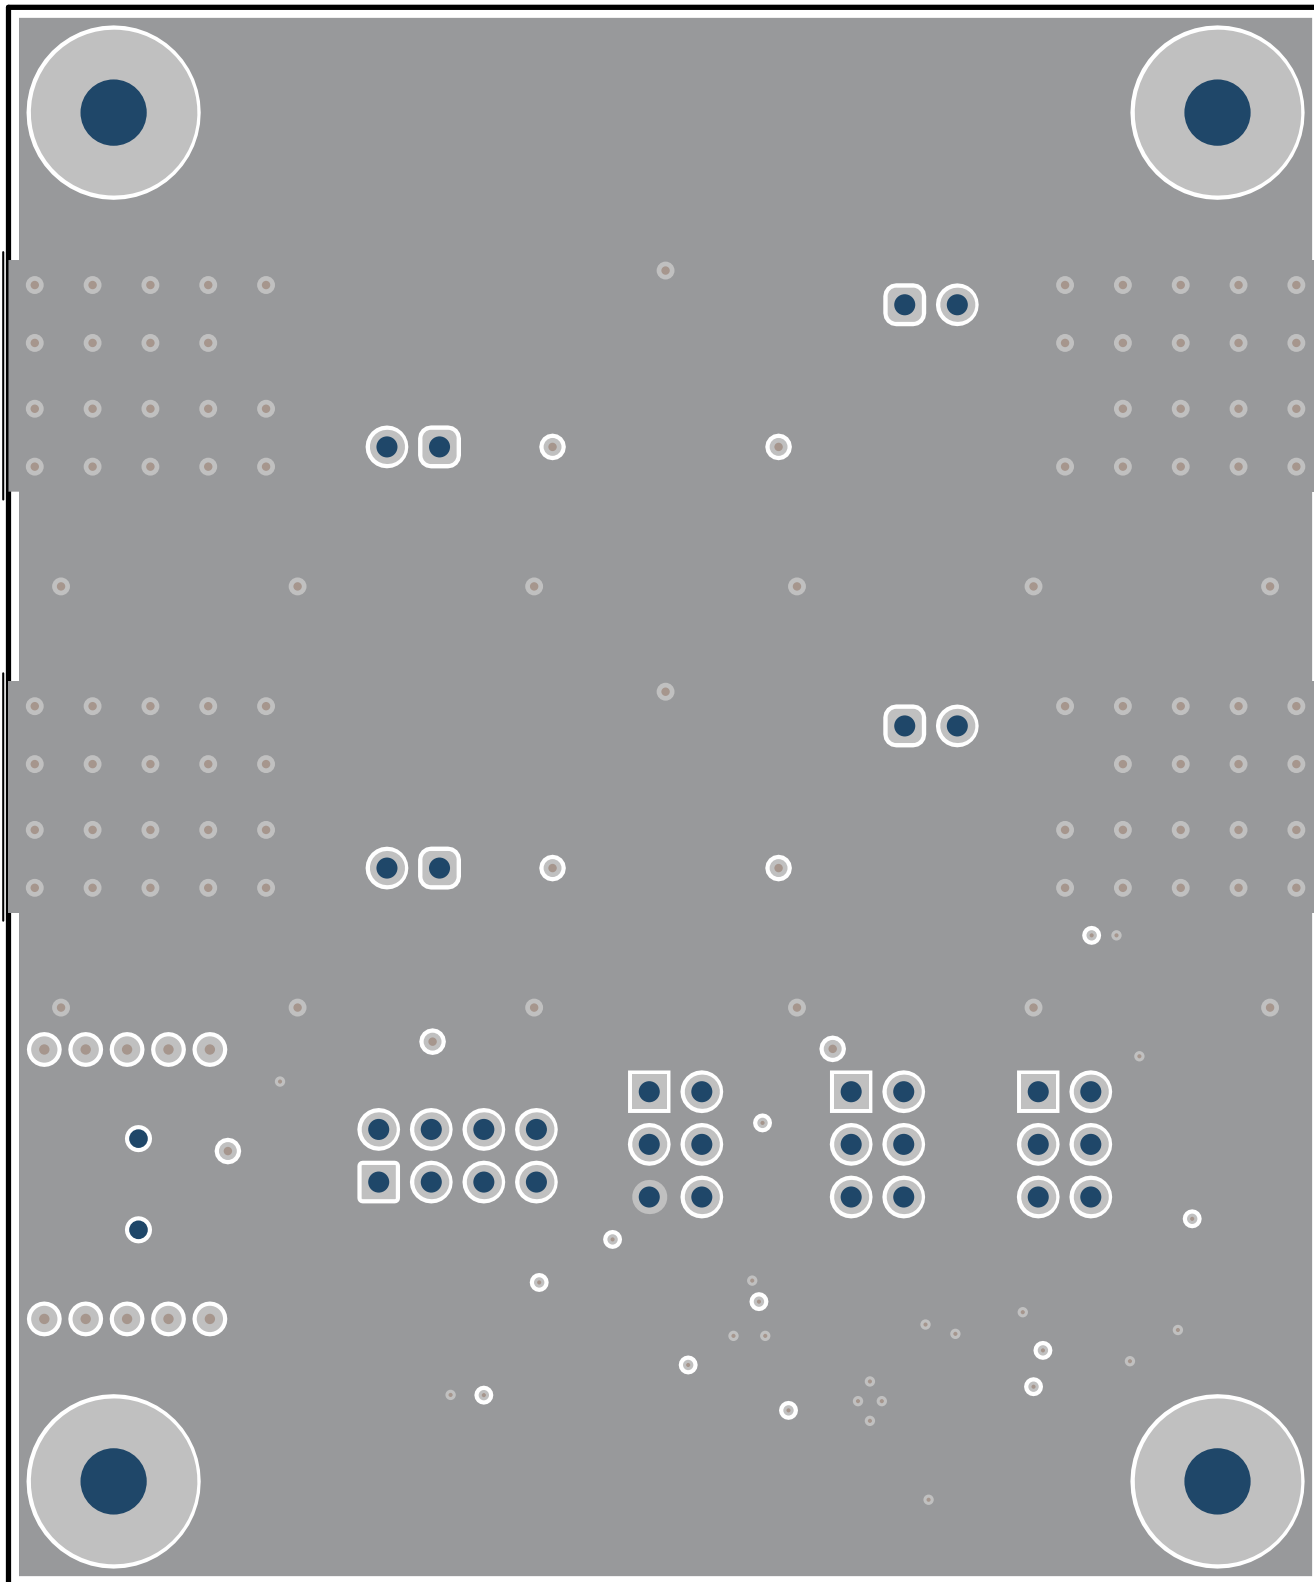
CDC6 EVM 的 PCB 布局示例 - 接地层
